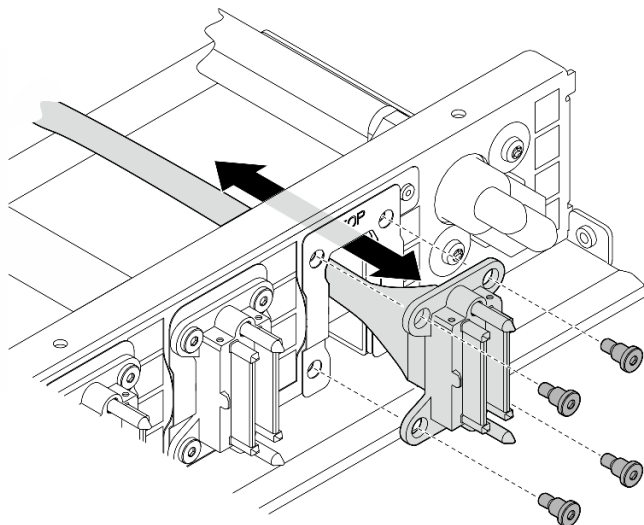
Módulo de E/S frontal, painel integrado de diagnósticos, gerenciamento de GPU ou instalação de cabo de sinal
